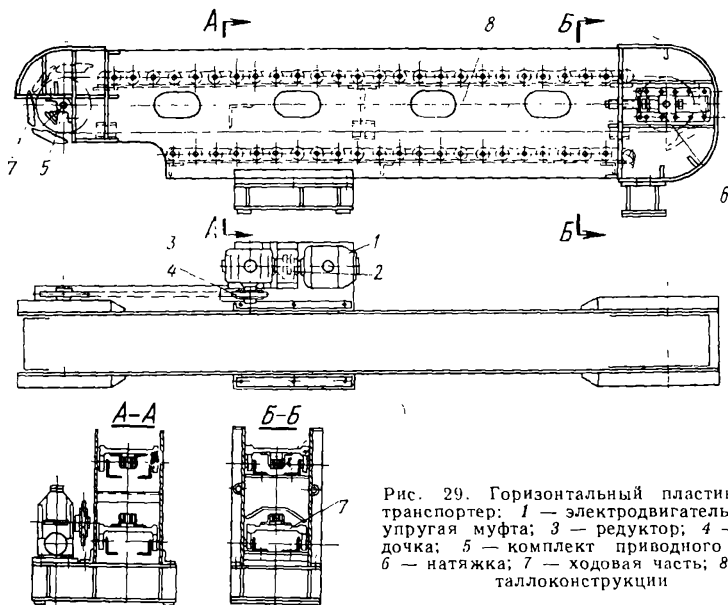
Горизонтальный пластинчатый транспортер: 1 — электродвигатель; 2 — упругая муфта; 3 — редуктор; 4 — звездочка; 5 — комплект приводного вала; 6 — натяжка; 7 — ходовая часть; 8 — металлоконструкция
